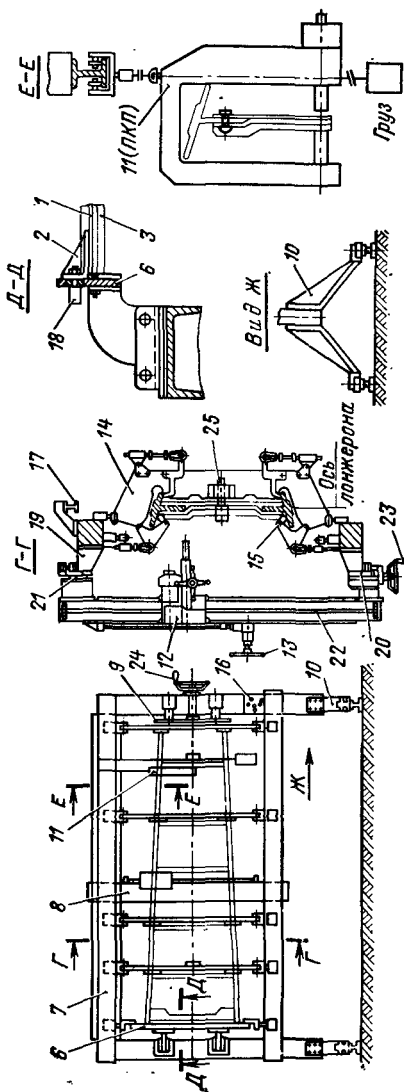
Схема базирования, схема сборки и сборное приспособление для сборки лонжерона
